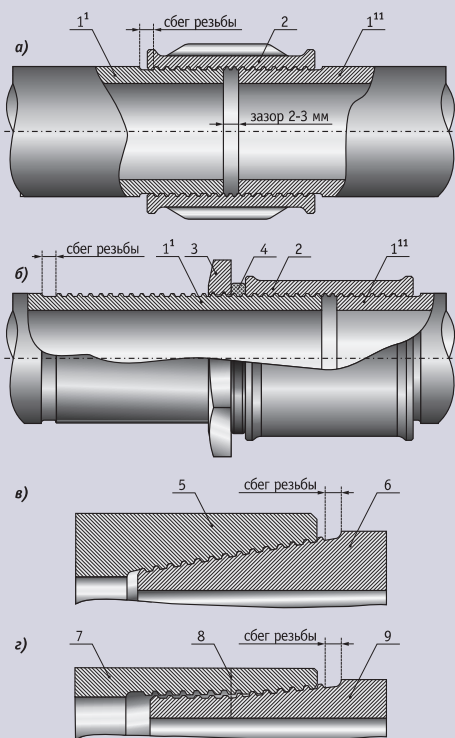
Схемы трубных резьб и соединений: а) на коротких цилиндрических резьбах; б) на цилиндрических короткой и длинной резьбах (сгон); в) коническая — коническая резьба; г) цилиндрическая — коническая резьбы
